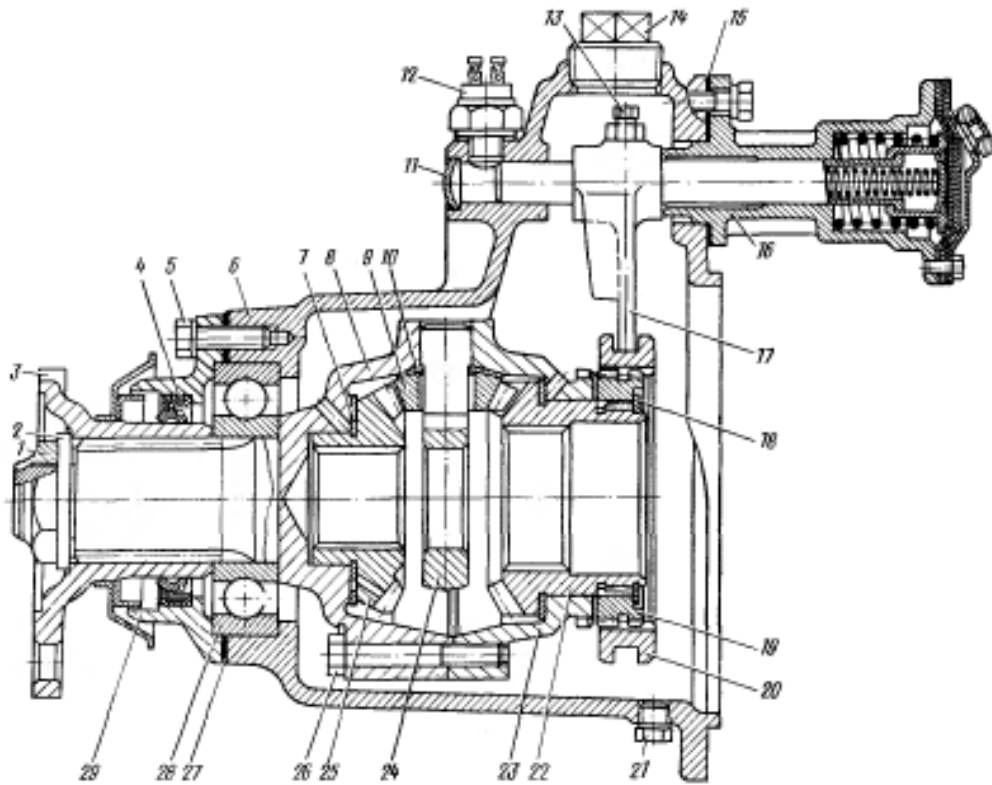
Міжосьовий диференціал: 1 – гайка; 2 – шайба; 3 – фланець; 4 - манжета; 5 – болт; 6; картер міжосьового диференціалу; 7, 10 – опорні шайби; 8 – передня чашка; 9 – сателіт з бронзовою втулкою; 11 – заглушка; 12 – датчик блокування; 13 - установочний гвинт; 14 – заливна пробка; 15 – прокладка; 16 – механізм блокування; 17 – вилка муфти; 18 – стопорне кільце; 19 – зубчата муфта; 20 - муфта блокування; 21 – зливна пробка; 22 – шестерня приводу середнього мосту; 23 – задня чашка; 24 – хрестовина; 25 – шестерня приводу заднього мосту; 26 - болт кріплення чашок диференціалу; 27 – прокладка; 28 – підшипник; 29 – кришка підшипника.
